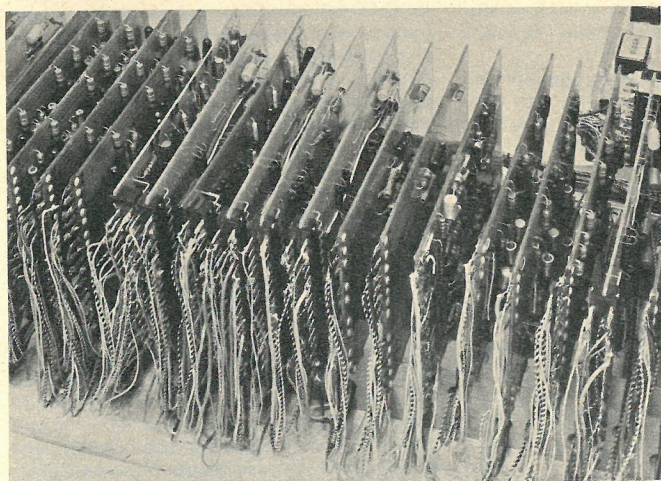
Blick auf die Druckplatinen des Rechners, gebaut für den Wettbewerb „Jugend forscht“
